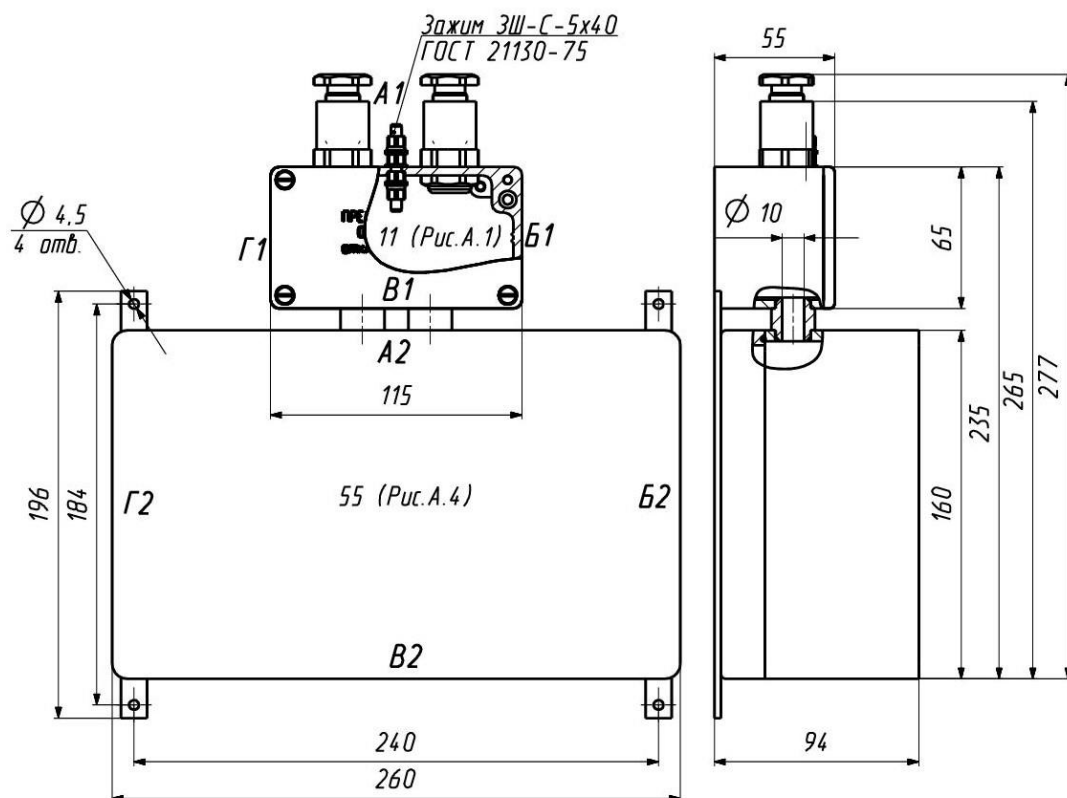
Блок корпусов и коробка клеммная ЕхБКР-А11В1/А55А2 (скрепление корпусов типоразмеров 11 и 55 сторонами В1 и А2) – вариант 9
